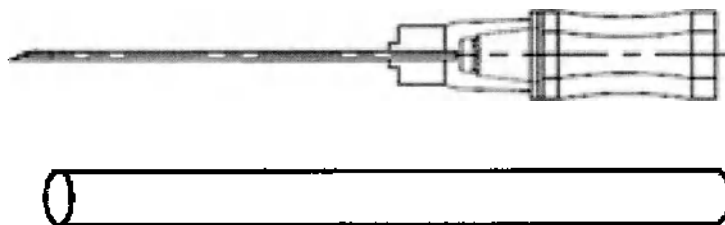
Общая конструкция изделия и схематичная форма нити
